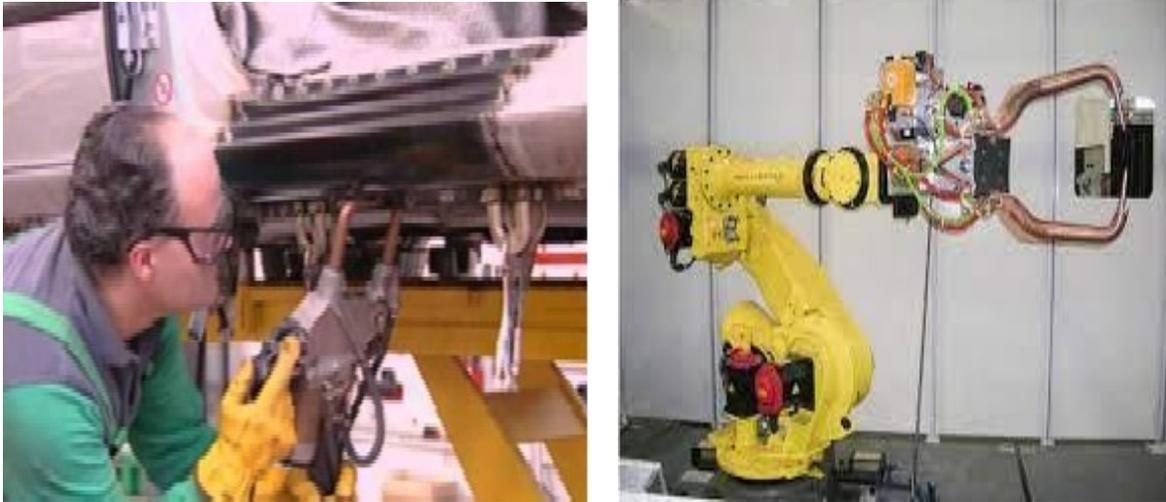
Equipo de soldadura portátil manual y robotizado.
